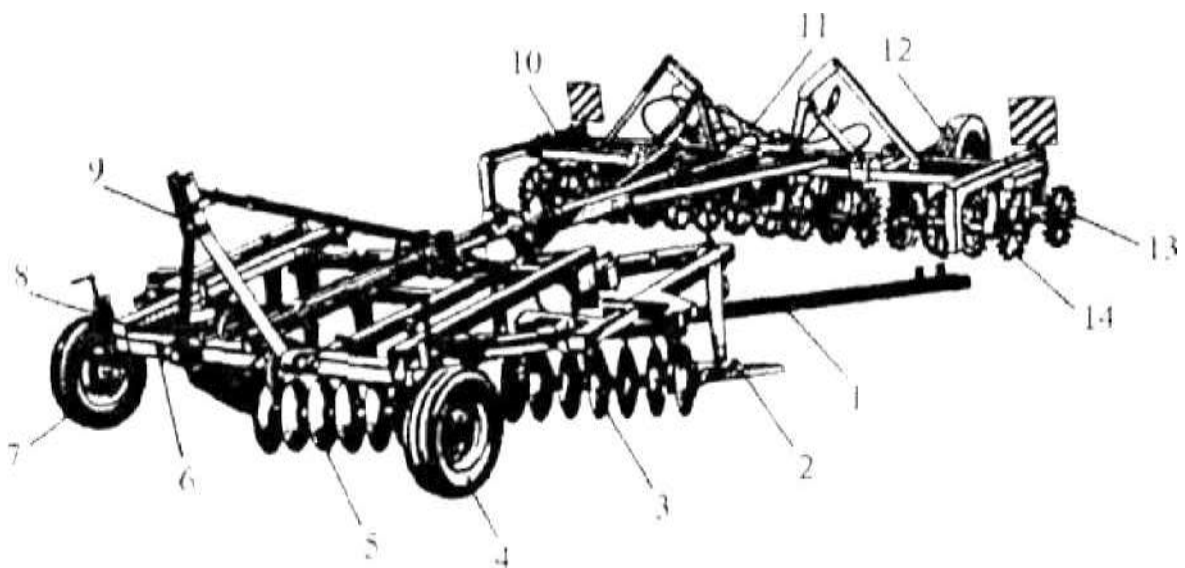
Агрегат комбінований ґрунтообробний АКП-5: 1 – пристрій для вирівнювання поверхні поля; 2 – плоскорізальні лапи; 3, 5 – батареї дискові секційні; 4, 7, 12 – пневмоколеса; 6 – рама передня; 8 – регулювальний механізм; 9 – начіпний пристрій; 10 – рама задня; 11 – шланги високого тиску гідросистеми; 13, 14 – катки кільцеві, шпорові.
